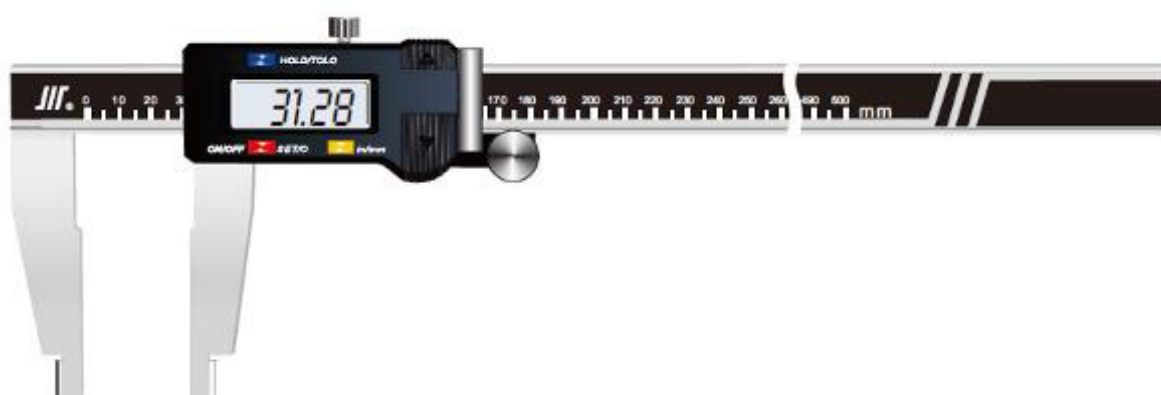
Общий вид штангенциркулей модели ШЦЦ-III
